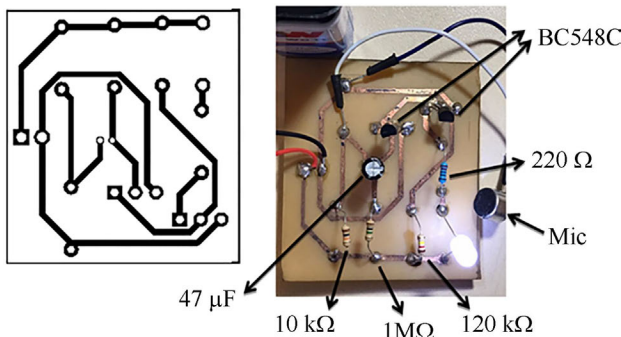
(a) Desenho para confecção da placa de circuito impresso. (b) Placa pronta, com todos os componentes soldados.
